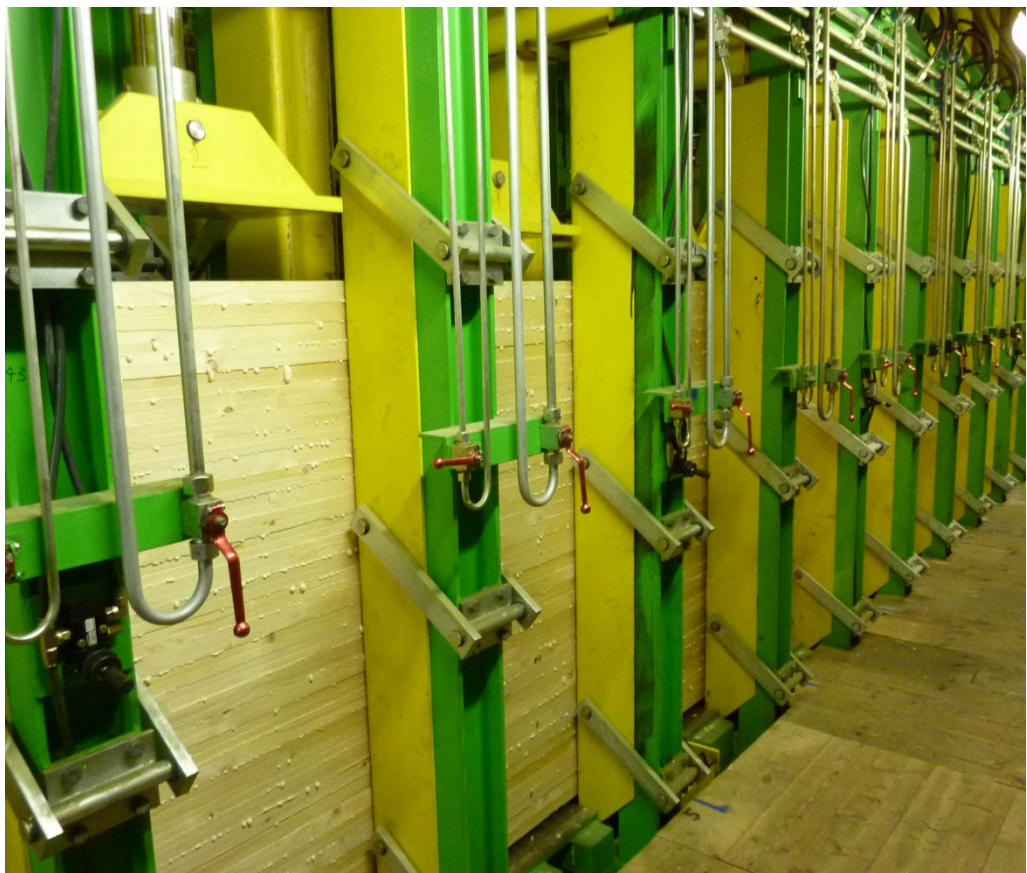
Presse hydraulique (source: Roth Burgdorf AG)
